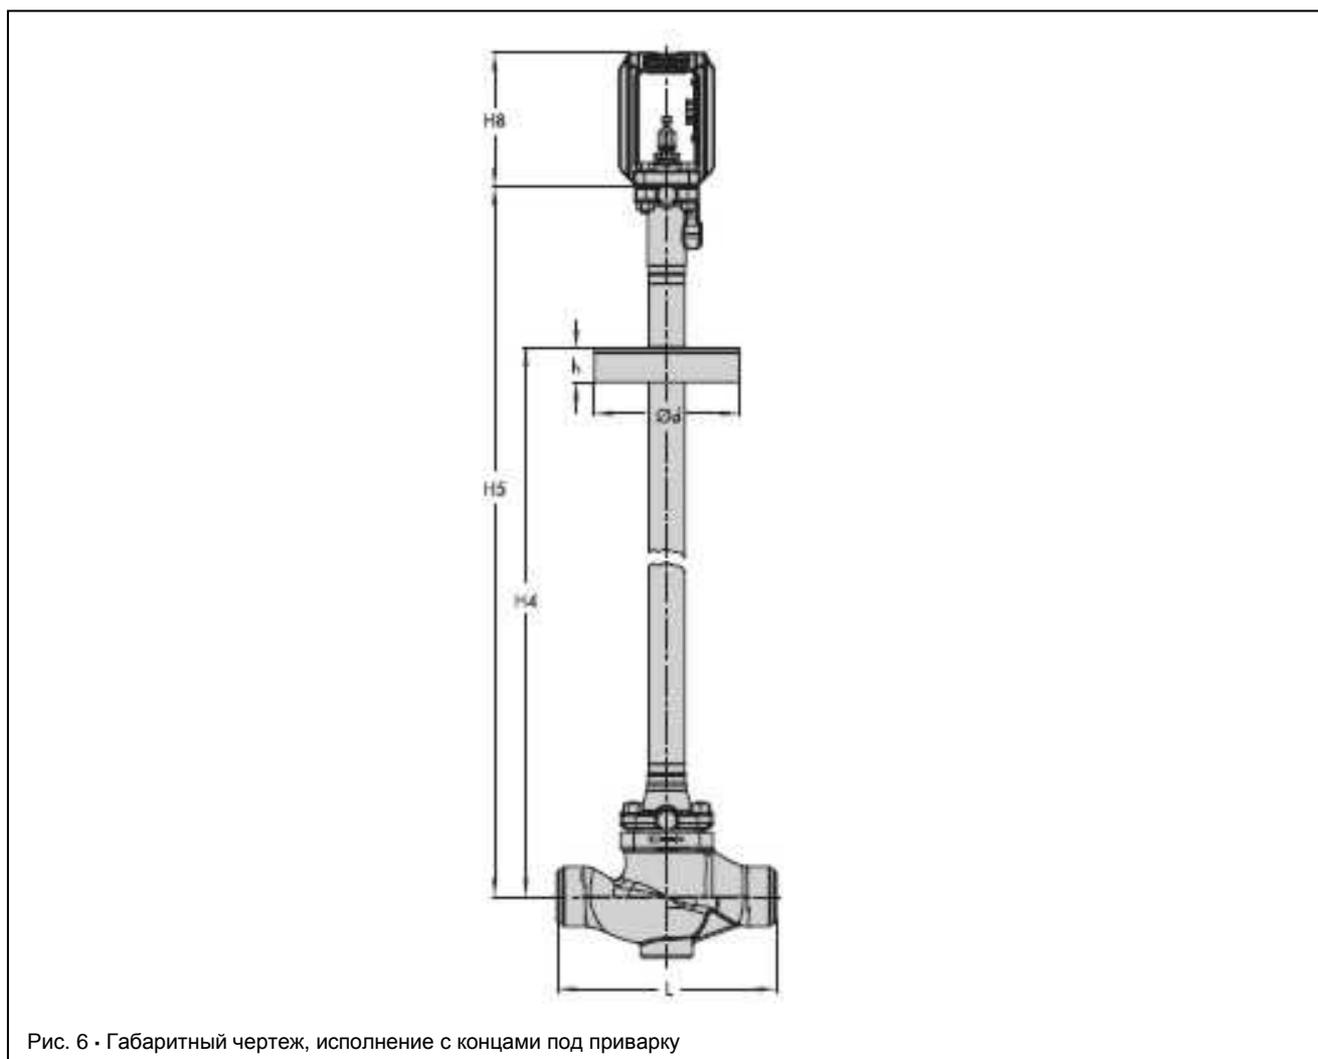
• Габаритный чертеж, исполнение с концами под приварку
